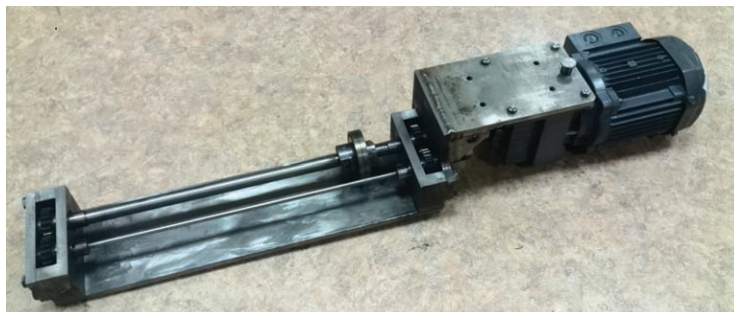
Приспособление для испытаний модельных образцов зубчатых колес
